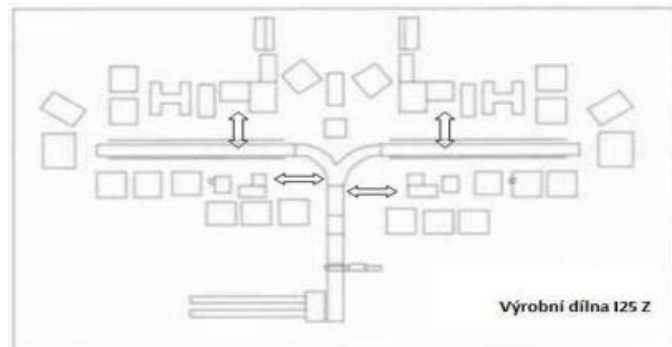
Obecná ilustrace layoutu výrobní haly [10]
